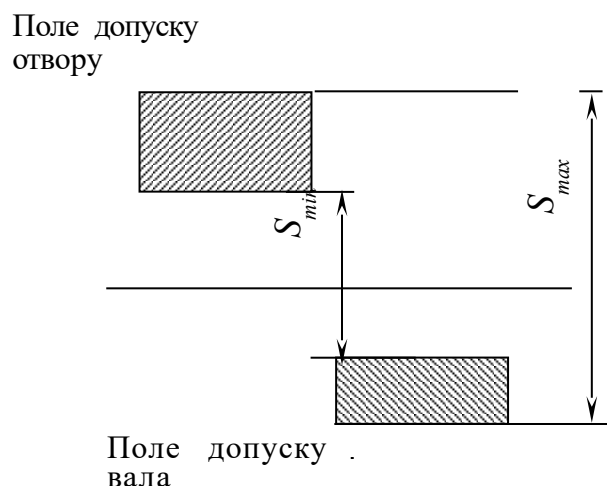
Поля допусків посадки із зазором
